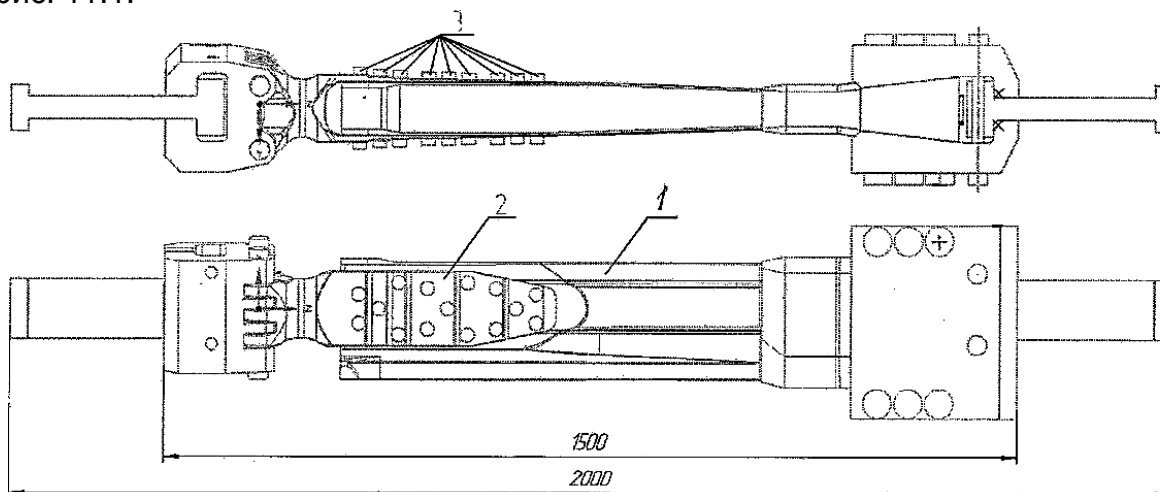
Общий вид и габаритные размеры объекта испытаний с соединительными захватами
